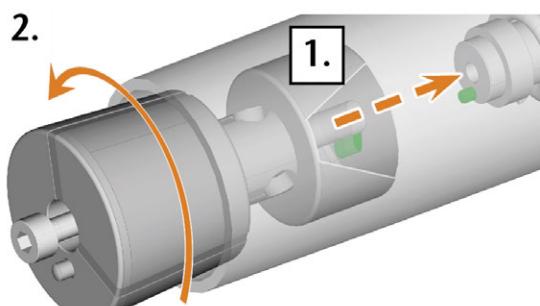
INSÉRER LA PINCE DE SERRAGE DANS LE SUPPORT DE PIÈCES BRUTES
